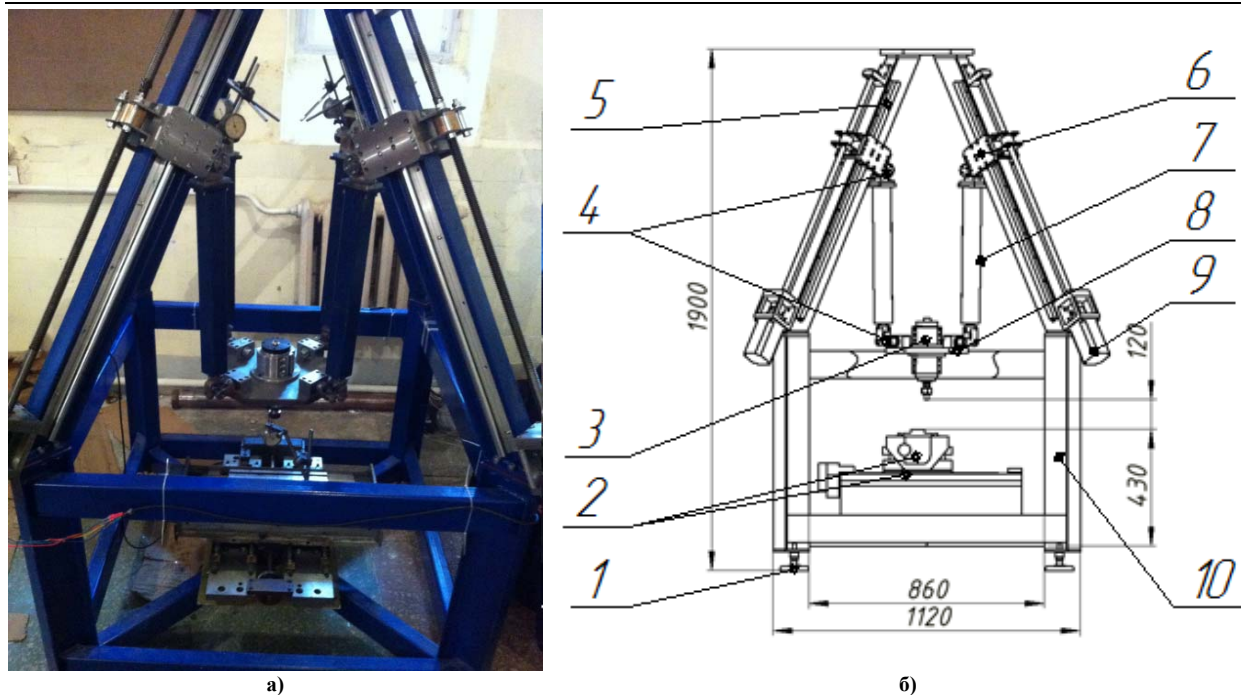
Свердлильно-фрезерний верстат пірамідальної компоновки: а – фото зі встановленими індикаторами; б – загальний вид – опора 1, хрестовий стіл 2, мотор-шпиндель 3, шарнір 4, напрямна 5, каретка 6, штанга постійної довжини 7, рухома платформа 8, лінійний двигун 9, каркас 10.
